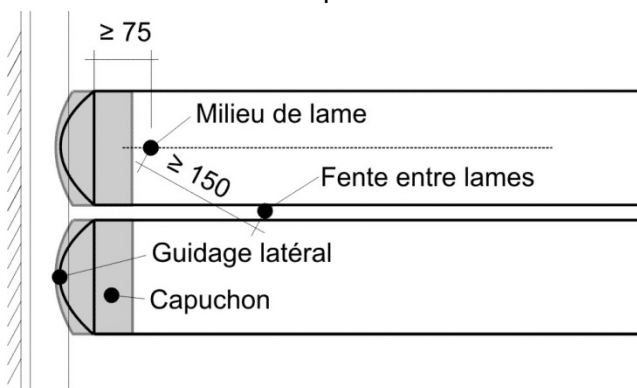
Points d'impact sur une couverture de piscine (dimensions en millimètres).
